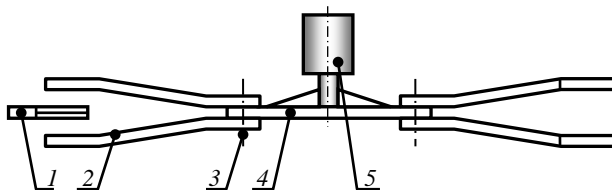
Схема ротора пастбищной косилки Schulte с неподвижным противорежущим ножом: 1 – неподвижный нож; 2 – подвижные ножи; 3 – болты; 4 – несущая часть ротора; 5 – привод
